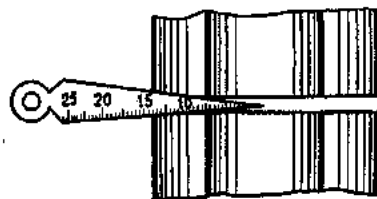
Металлический клин с делениями для измерения стыковых зазоров
